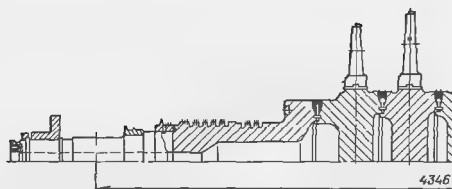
Сварной ротор газовой турбины ГТ-12-650 (ЛМЗ)
